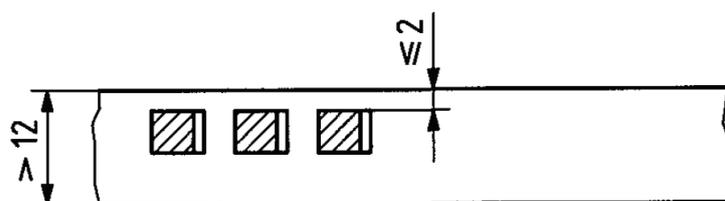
Расположение мест вырезки образцов для испытаний на ударный изгиб для листового проката согласно Eurocode 10025–1
